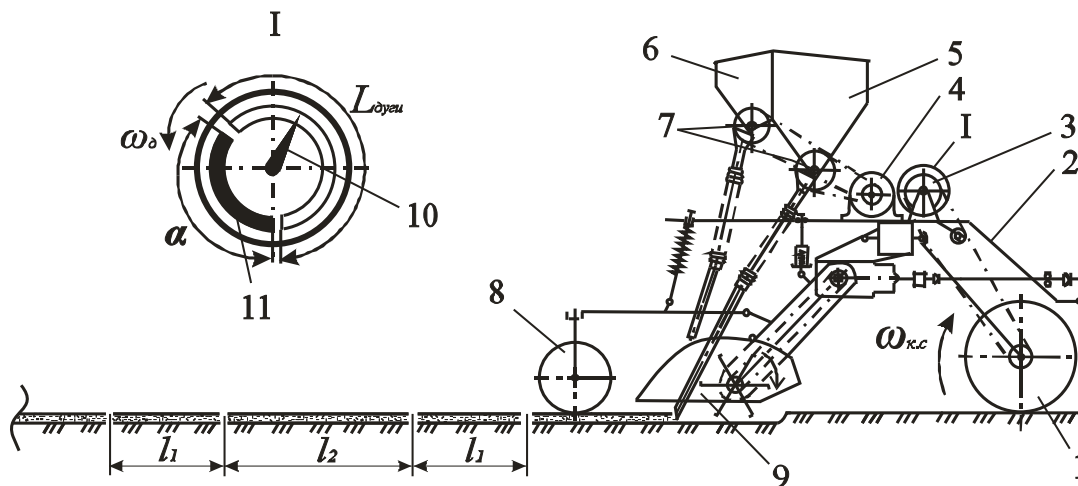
Конструктивно-технологическая схема дернинной сеялки: 1 – опорно-приводное колесо, 2 – рама; 3 – орган управления, 4 – исполнительный механизм, 5,6 – ящики для семян, 7 – валы высевующих аппаратов, 8 – прикатывающий каток, 9 – фрезерная секция, 10 – контактный рычаг, 11 – контактный сектор
